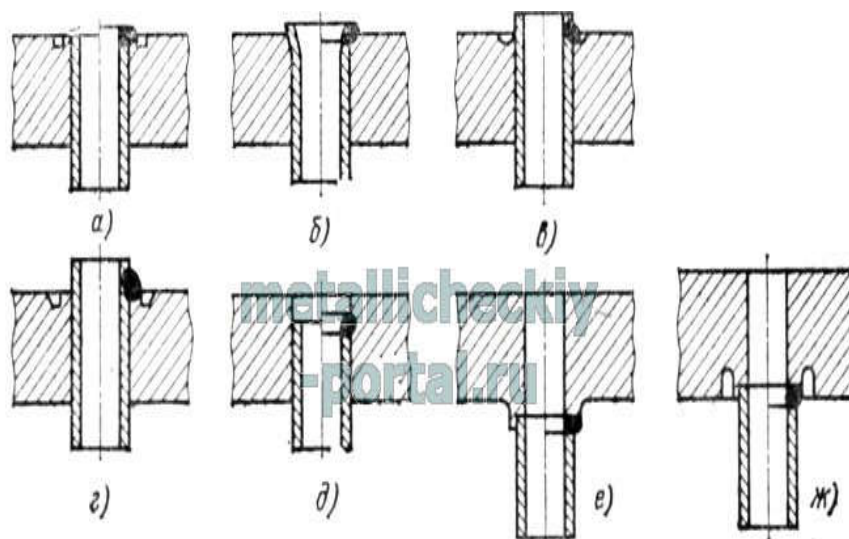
Варіанти з'єднання труб з трубними дошками дуговими способами зварювання
